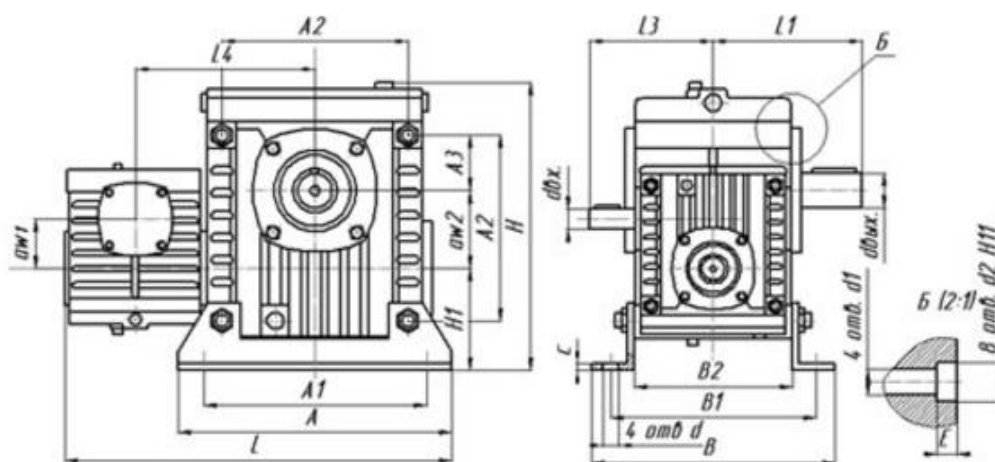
Габаритные и присоединительные размеры редукторов Ч2-40/63
